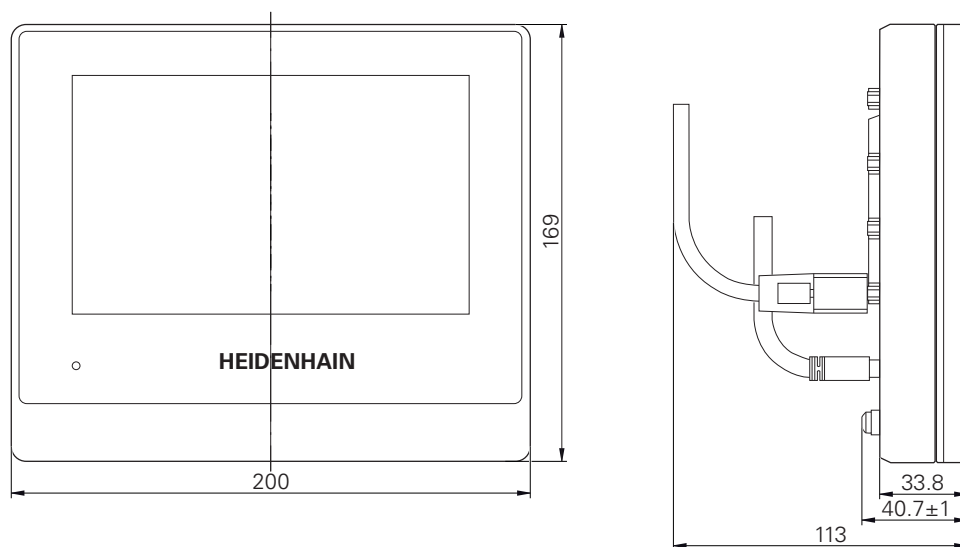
Dimensioner för enhetens hölje med ID 1089178-xx
